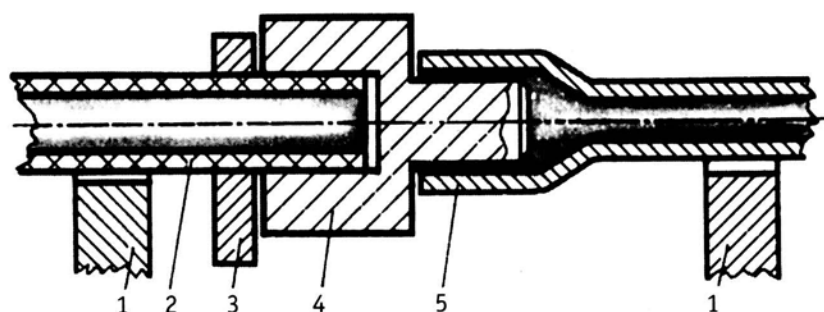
Устройство для сварки в раструб:
